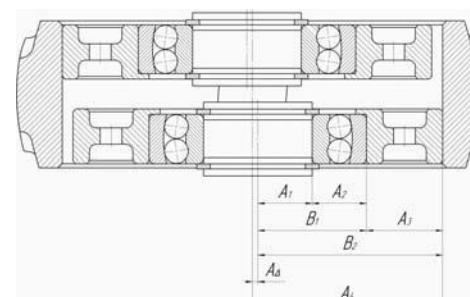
Размерная цепь "Входной вал – самоустанавливающийся подшипник – диск – колесо прецессирующее"
